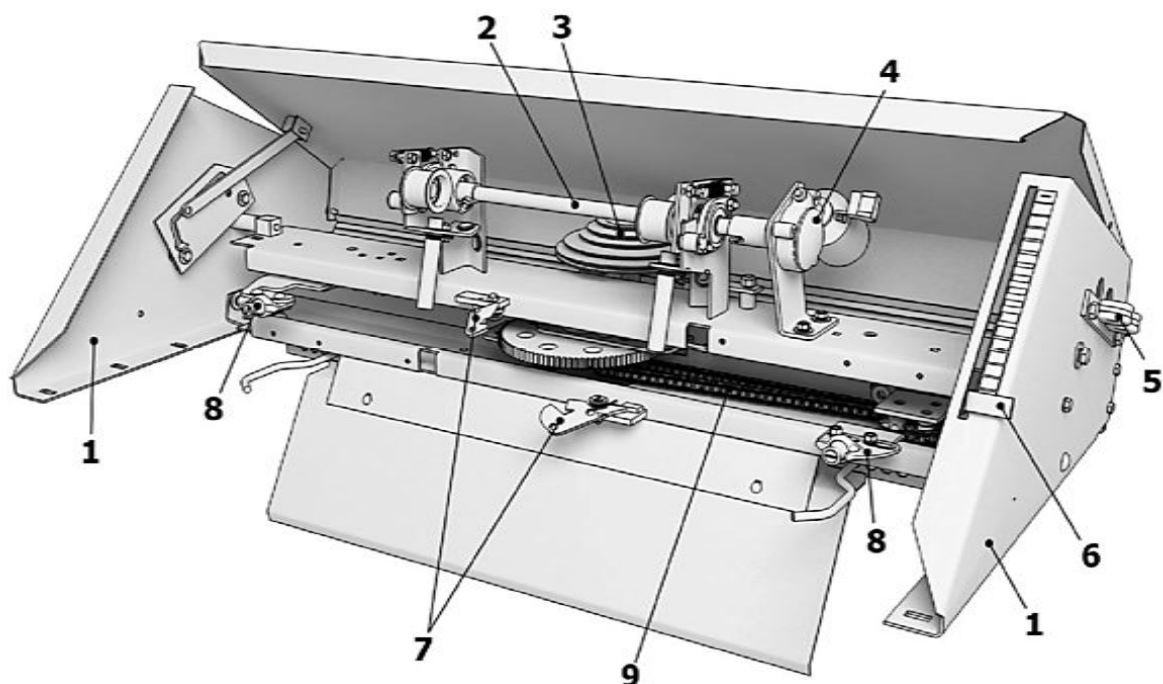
Аппарат обматывающий: 1 – каркас; 2 – подающий вал; 3 – шкив приводной; 4 – электродвигатель с редуктором; 5 – глазки шпагата; 6 – механический указатель плотности рулона; 7 – нож; 8 – каретка с поводком; 9 – цепи
